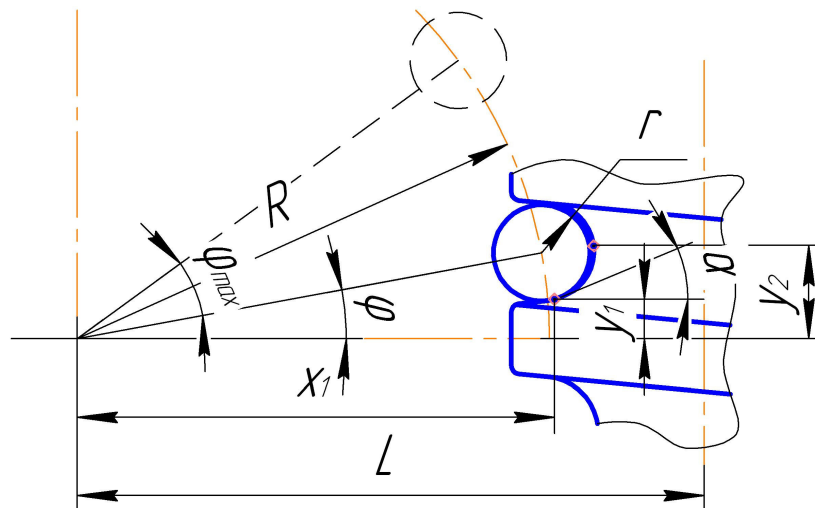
Розрахункова схема для визначення профілю черв'яка
